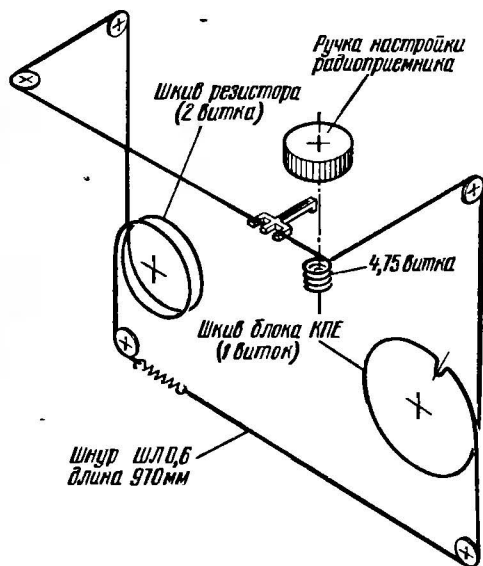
Кинематическая схема верньерного устройства РПУ (А1) магнитолы «Соната РМ-323С»
